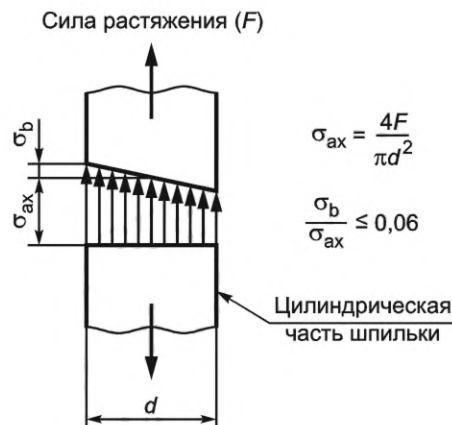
Распределение напряжений в цилиндрической части шпильки
